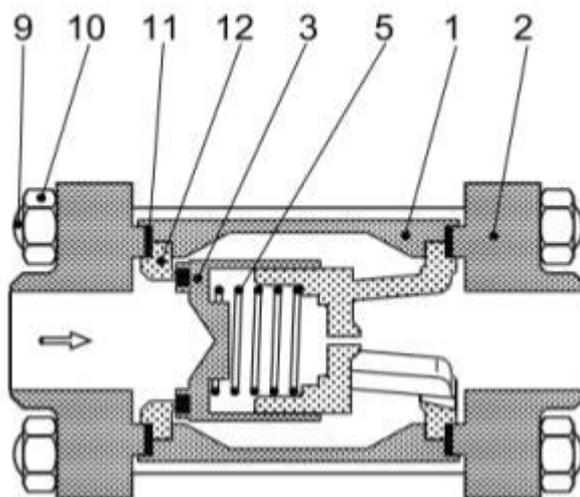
Клапан NRVA: 1 – корпус; 2 – фланцы; 3 – конус клапана; 5 – пружина; 9 – болты; 10 – NUT; 11 – прокладка; 12 – посадочное седло.
